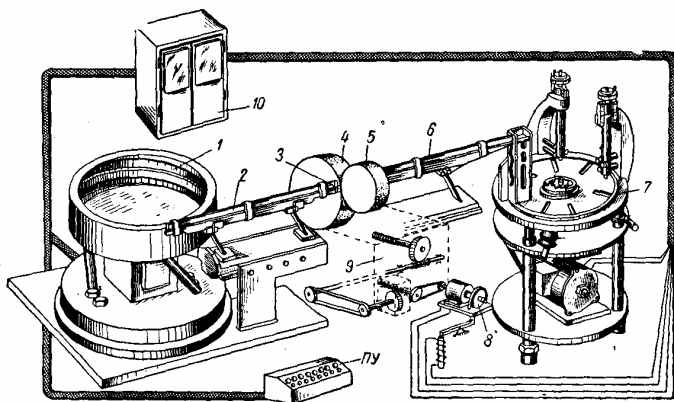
Схема работы автоподналадчика бесцентрово-шлифовального станка
